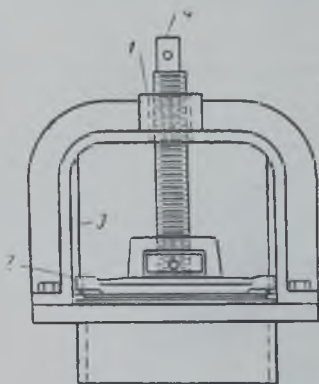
Клапан для удаления ила и грязи со дна резервуара (по материалам Rodney Hunt Machine Co.)
